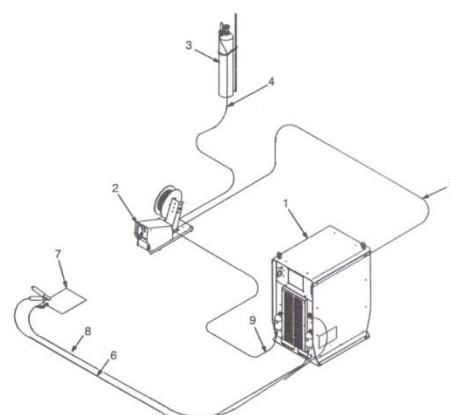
Схема подключения элементов цифрового исследовательского комплекса системы: 1 –источник питания; 2 –механизм подачи проволоки; 3 –газовый баллон; 4 –газовый шланг; 5 –сетевой кабель; 6 –отрицательный (–) сварочный кабель; 7 –образец; 8 –проводы измерения параметров режима сварки; 9 –положительный (+) сварочный кабель
